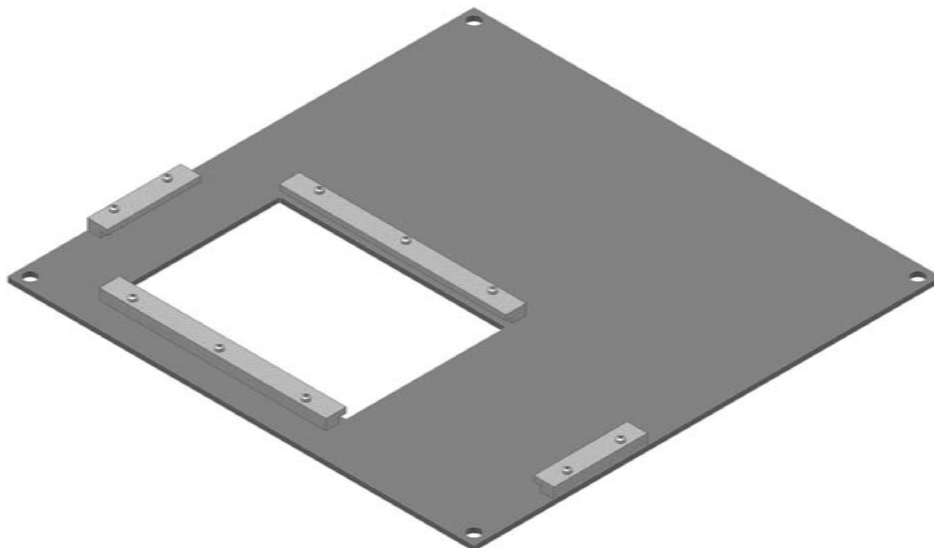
Gehäusedeckel mit Fenster und Glasdeckelhalterungen
